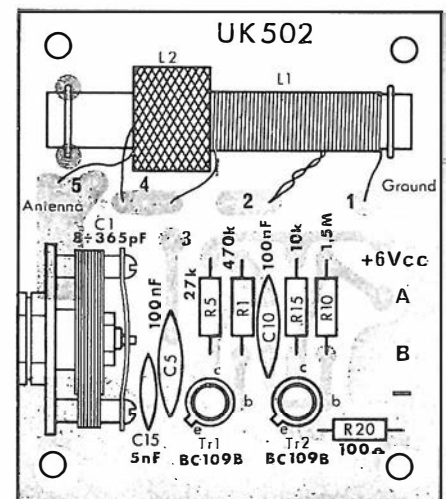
C - Il circuito stampato visto dal lato componenti e con gli stessi tutti inseriti. Per « trasparenza » è visto anche il rame sottostante (grigio). Le dimensioni del disegno sono quelle dell'apparecchio.
